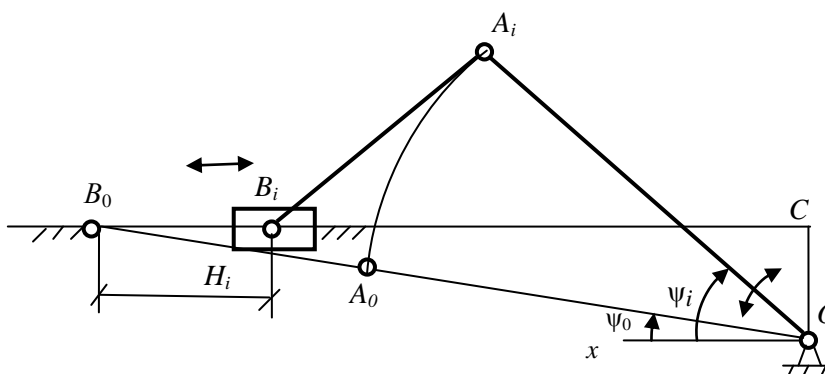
Коромысло-ползунный рычажный механизм и его кинематические параметры
